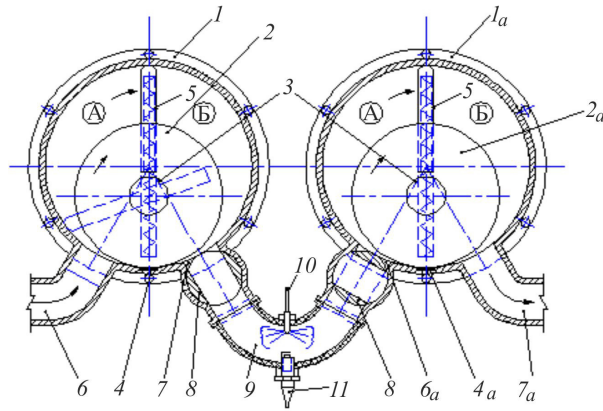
Роторный двухцилиндровый двухкамерный четырехтактный двигатель внутреннего сгорания
